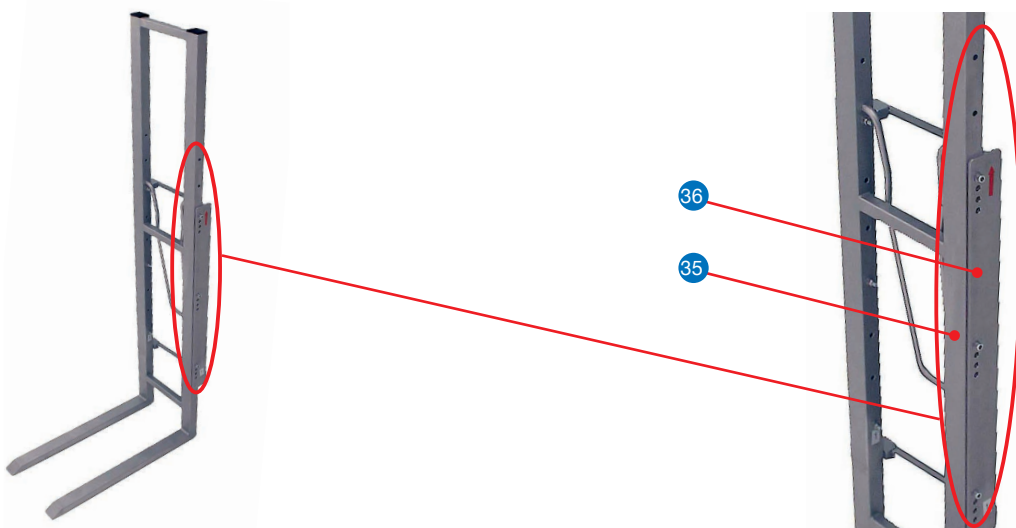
Standard-Höheneinstellung der Schwenkgabel in aufrechter Position
